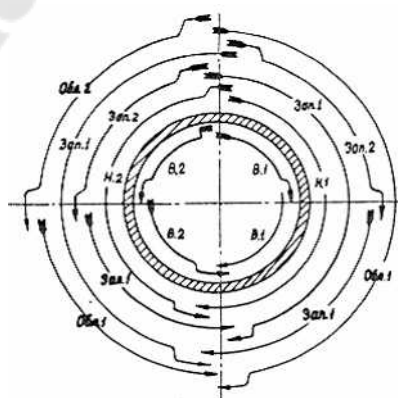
Последовательность наложения слоев при работе сварочных автоматов: Н - наружный корневой слой; В - внутренний корневой слой; Зап - заполняющий слой; Обл - облицовочный слой (цифра после обозначения слоя указывает на очередность сварки данного участка в пределах слоя); → - направление сварки
